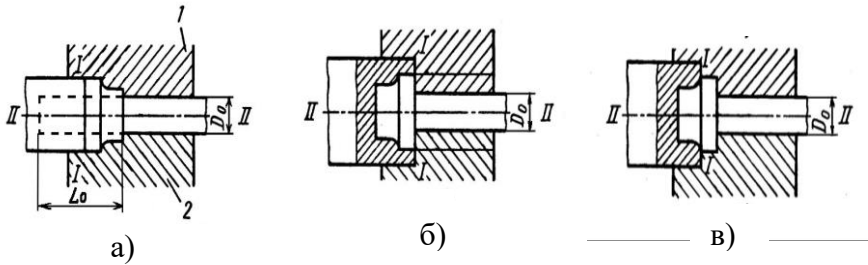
Схеми розміщення поковки у штампах (горизонтальний розріз штампів, вигляд зверху):
